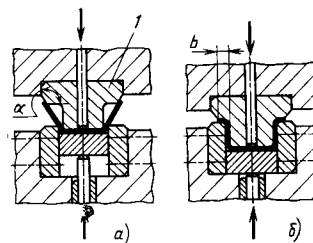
Разрез конструкции штампа для Ω -образной гибки деталей с полкой шириной $b \leq 5s$
